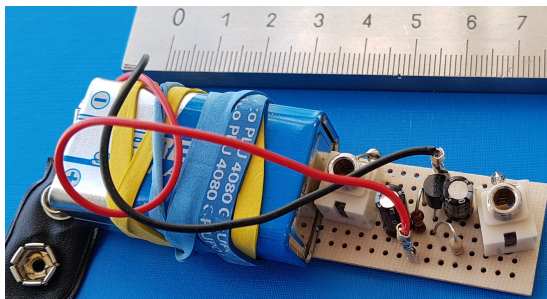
Circuito soldado sobre placa perforada para prototipos.
